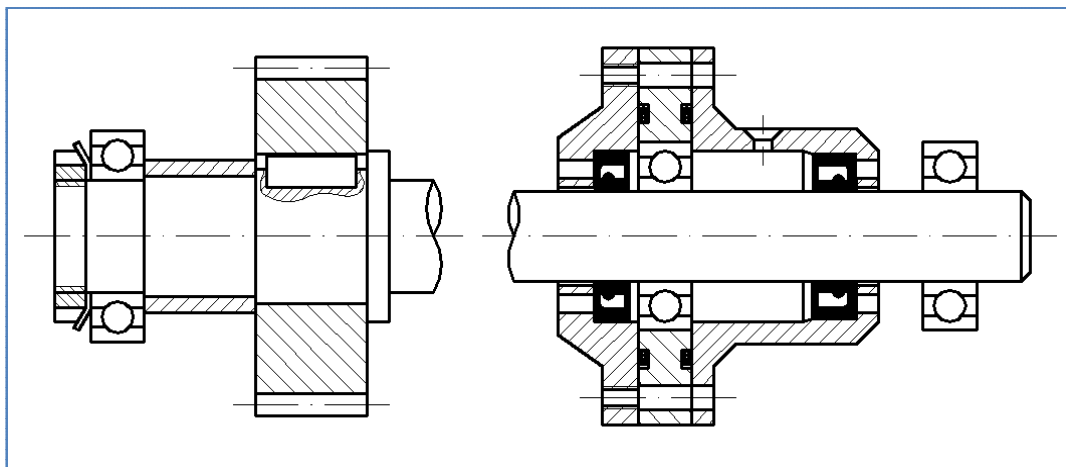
Croquis del diseño inicial del conjunto (partes izquierda y derecha)
